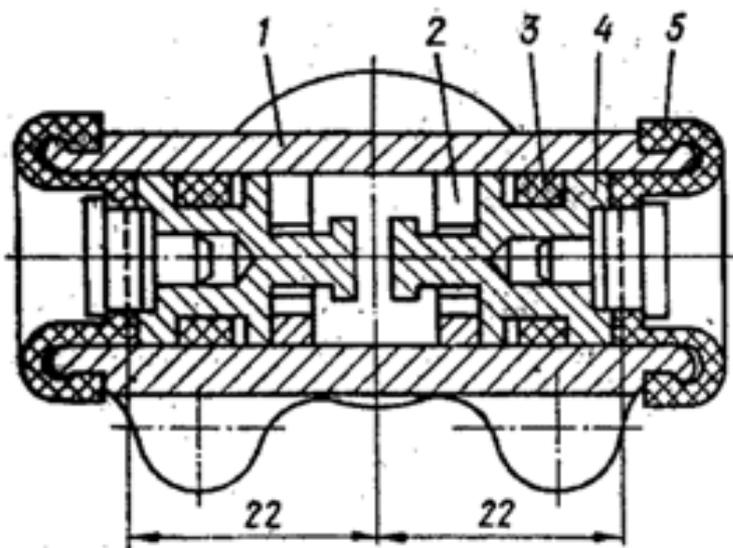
Цилиндр колесный заднего тормоза в сборе: 1 - цилиндр; 2 - кольцо упорное; 3 - манжета; 4 - поршень; 5 - колпак.
